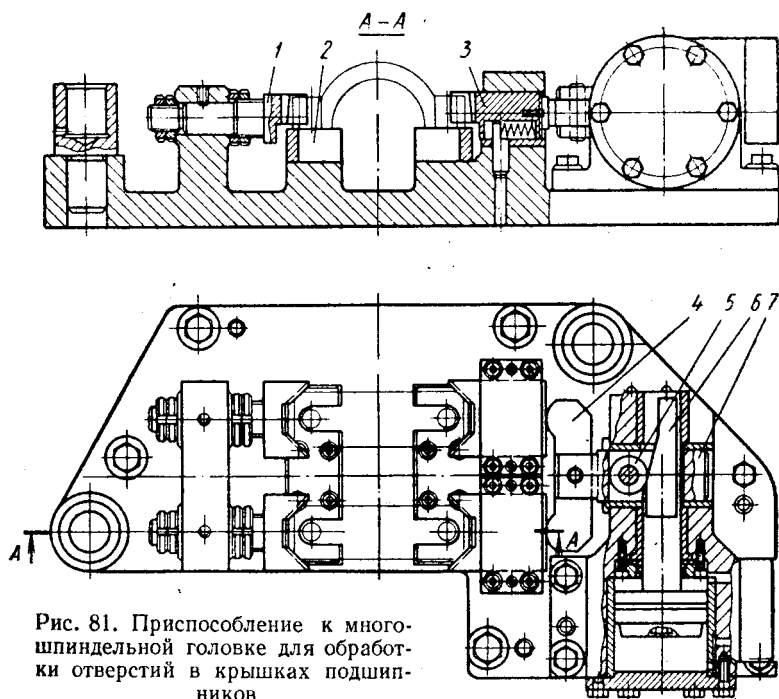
Приспособление к многшпindleйной головке для обработки отверстий в крышках подшипников
